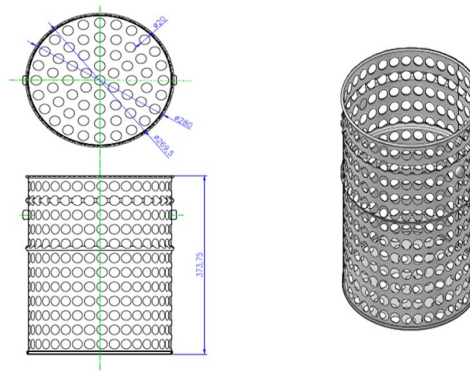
Drawing Autocad mesin mixer bagian penutup
